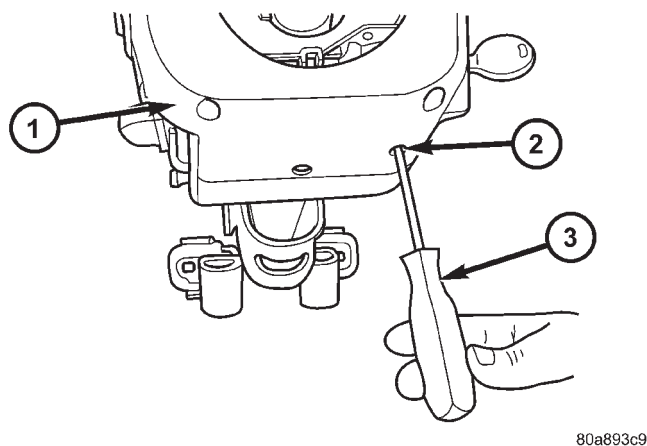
DESMONTAJE DE CUBIERTA Y CILINDRO DE CERRADURA
